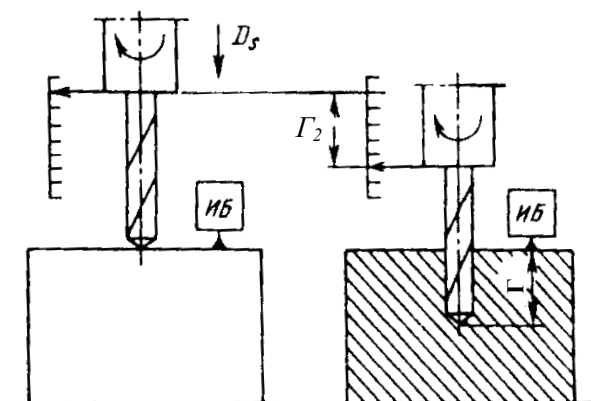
Схема получения размера заготовки от измерительной базы
